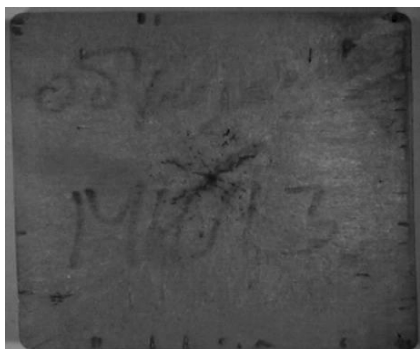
Макроструктура металу безперервнолитої заготовки 150 сталі марки СтЗнс пл. 254610 (№ 8)
